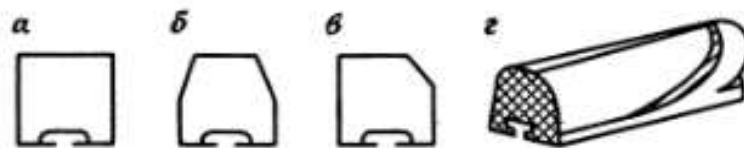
Конструкции лифтеров, применяемых в резиновых футеровках
